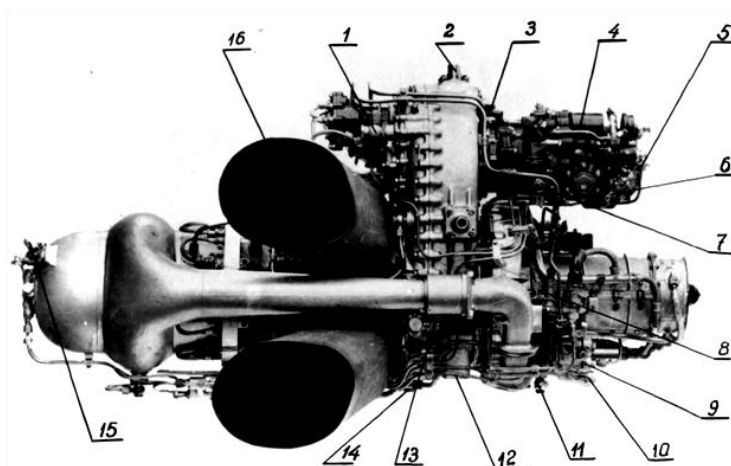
Двигатель ГТД-350 (вид справа)
